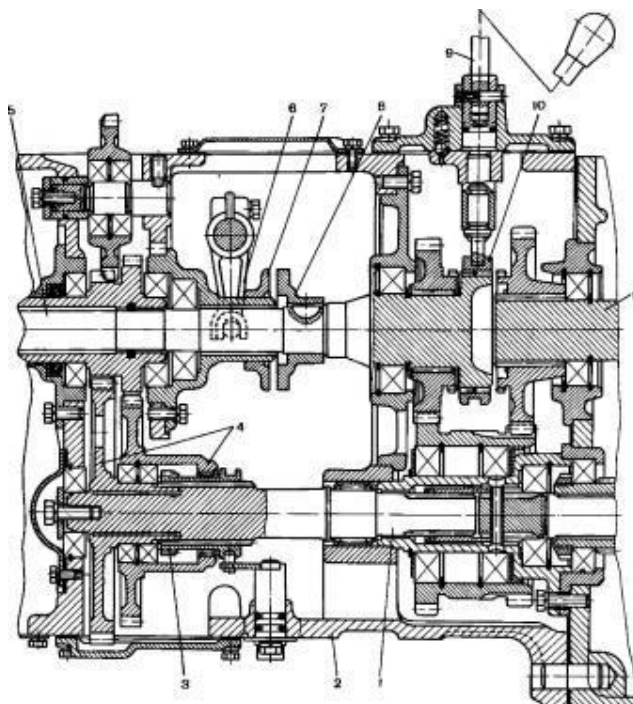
Понижающий редуктор и редуктор вала отбора мощности трактора МТЗ-80, 82.
